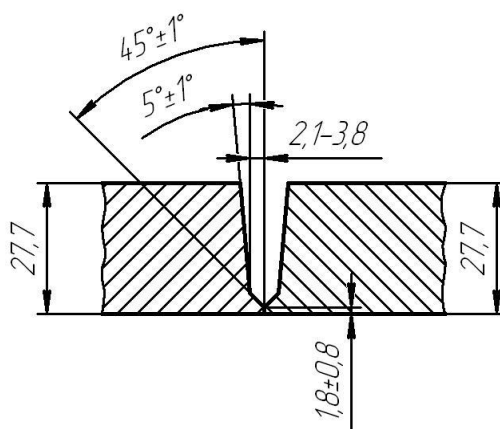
Подготовка кромок труб под сварку
